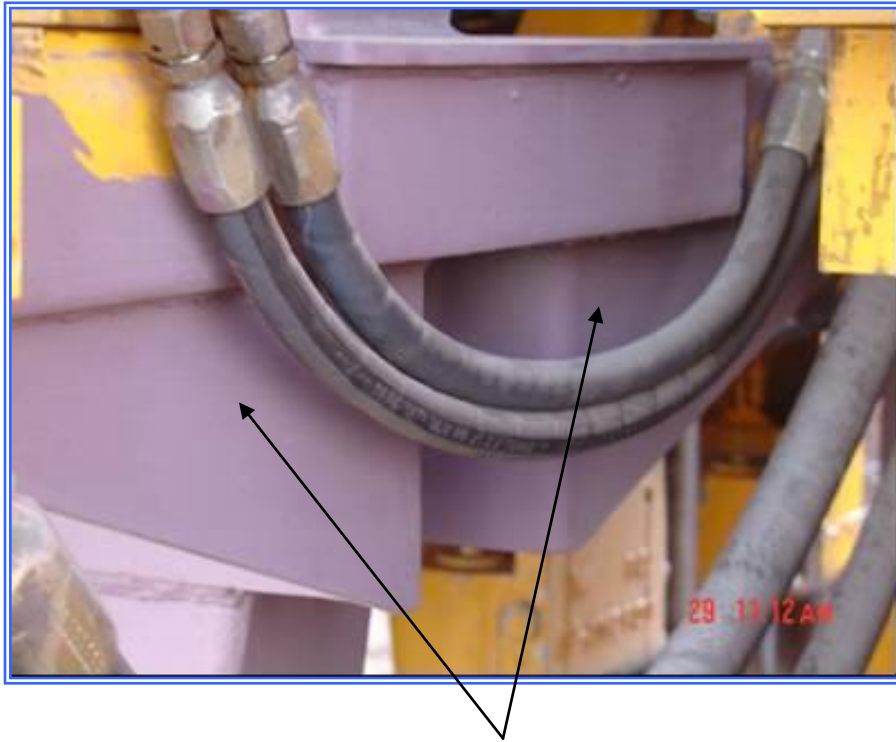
Pie de Amigos soldados para reforzar viga
